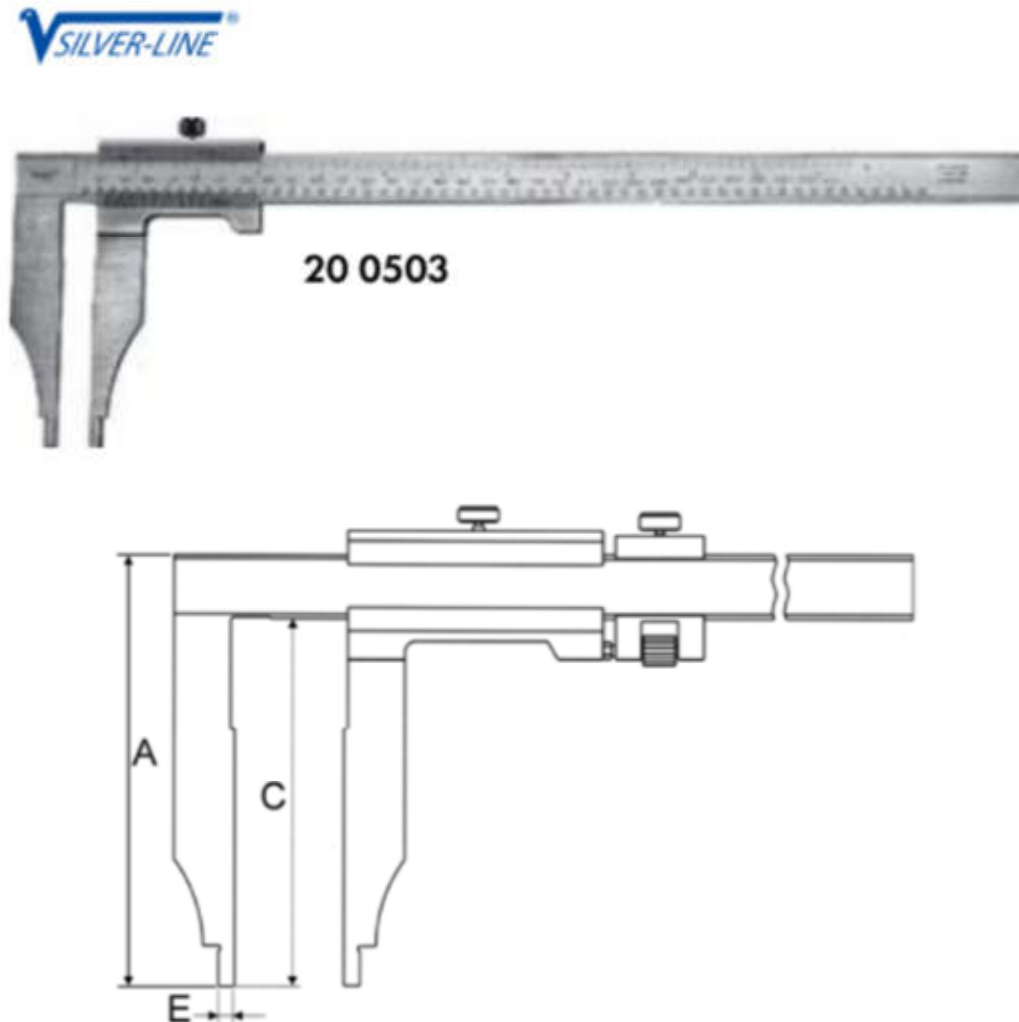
Штангенциркуль ШЦ-III для зовнішніх поверхонь [8]
